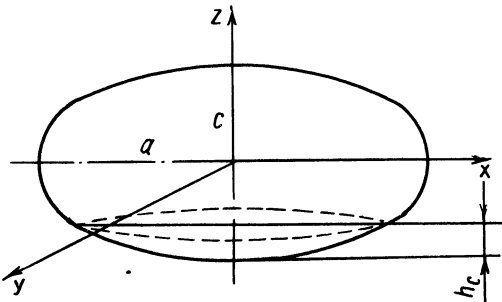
Схема внедрения абразивного зерна в поверхность детали
